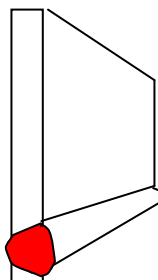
Profundidad de penetración aceptable, para soldaduras de placas a tope
